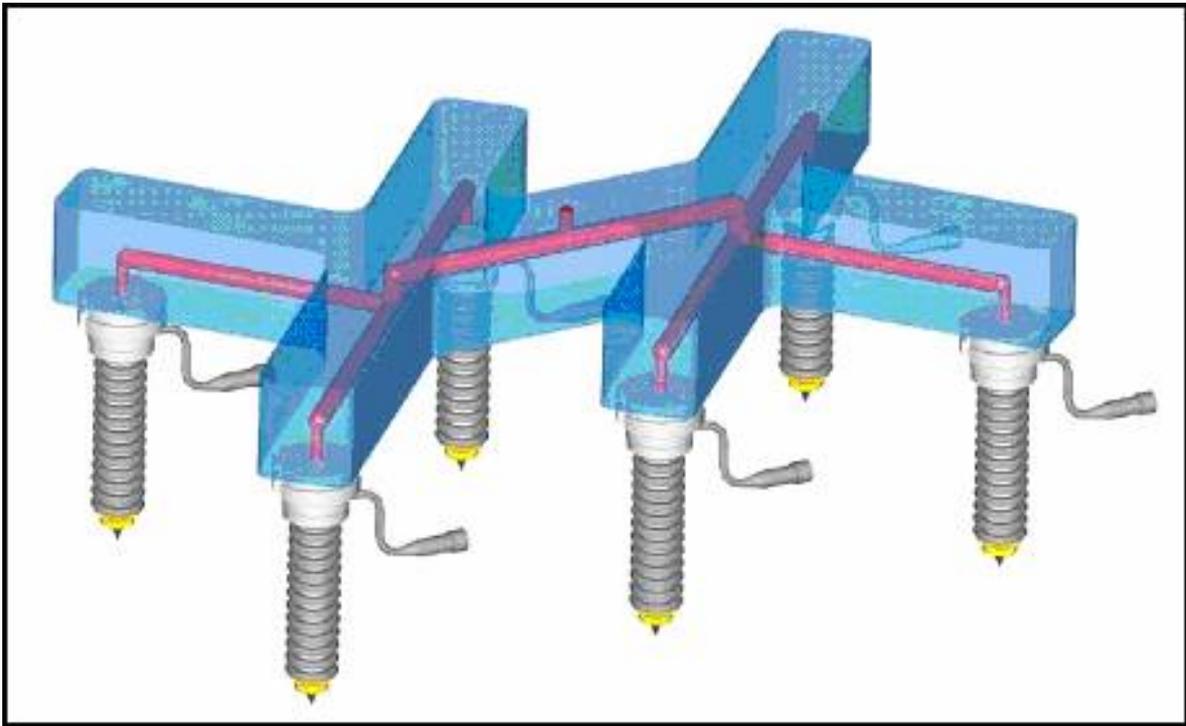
Sistema de colada caliente para moldes multicavidad o piezas con varios puntos de inyección
